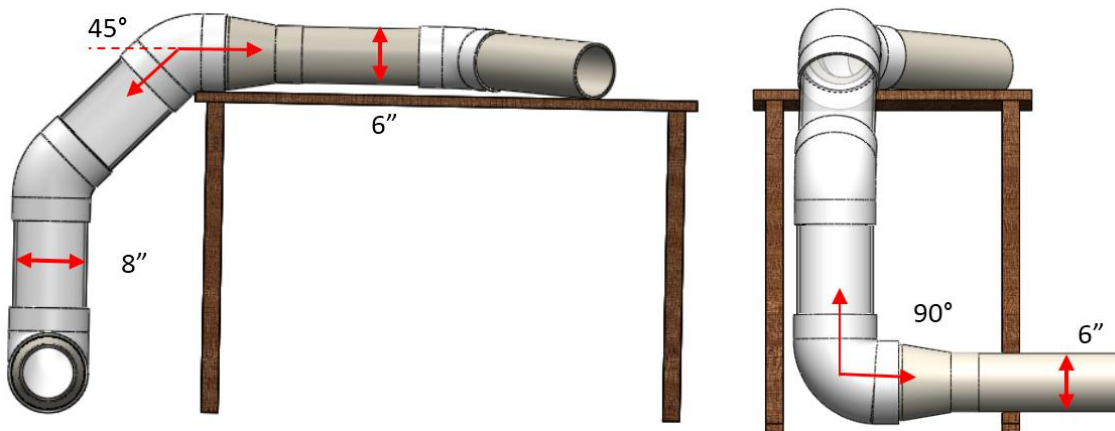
Diseño CAD de la maqueta con soporte. (Vistas isométricas: Posterior y Lateral Izquierda)
